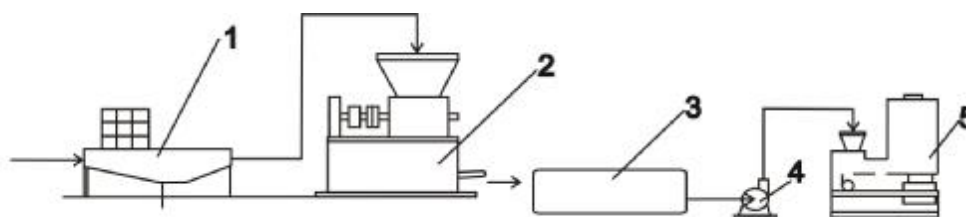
Технологическая схема предварительной подготовки отходов: 1 – стол разборки сырья; 2 – установка для предварительного измельчения пленки; 3 – ванна; 4 – пневмотранспорт; 5 – установка для непрерывной отмывки
